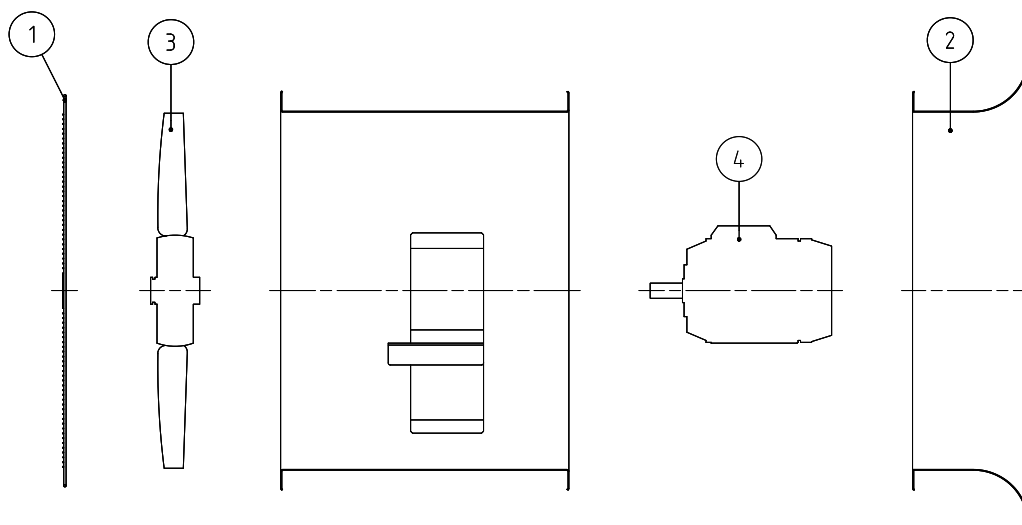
Explosionszeichnung des Ventilators in Ausführung 4
